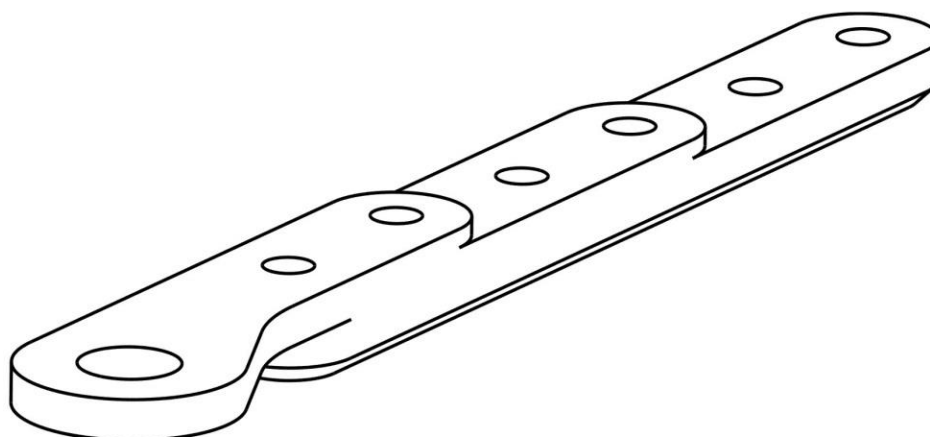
Opracovanie hlavných rozmerov závesu krídla
